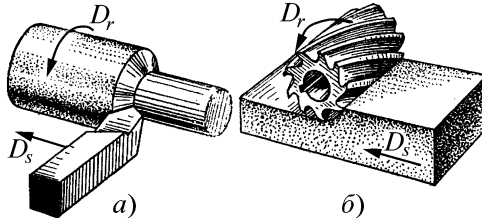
Схемы точения (а) и фрезерования (б)
